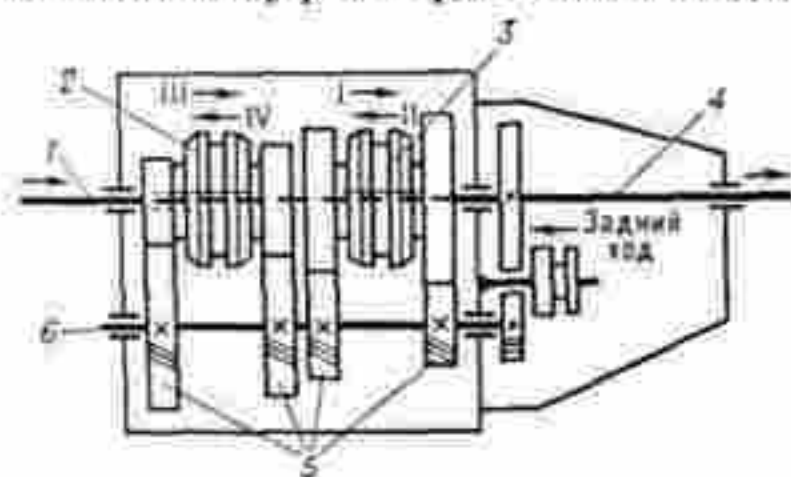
Схема автомобильной четырёхступенчатой (I—IV) коробки передач: 1 — первичный вал; 2, 3 — муфты с синхронизаторами; 4 — выходной вал; 5 — шестерни, входящие в зацепление с зубчатыми колёсами; 6 — вторичный вал.
